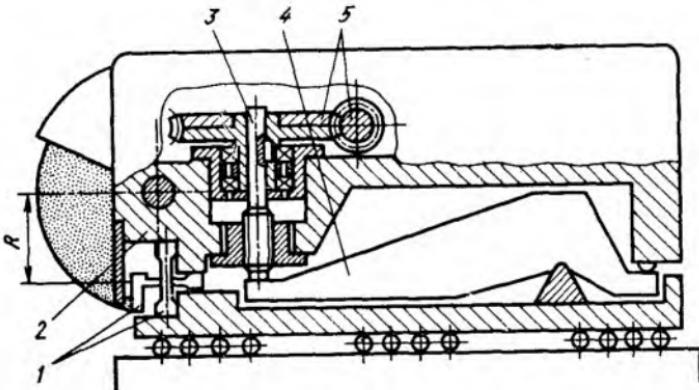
Шлифовальная бабка с механизмом микроподачи круглошлифовального станка ЗЕ153
